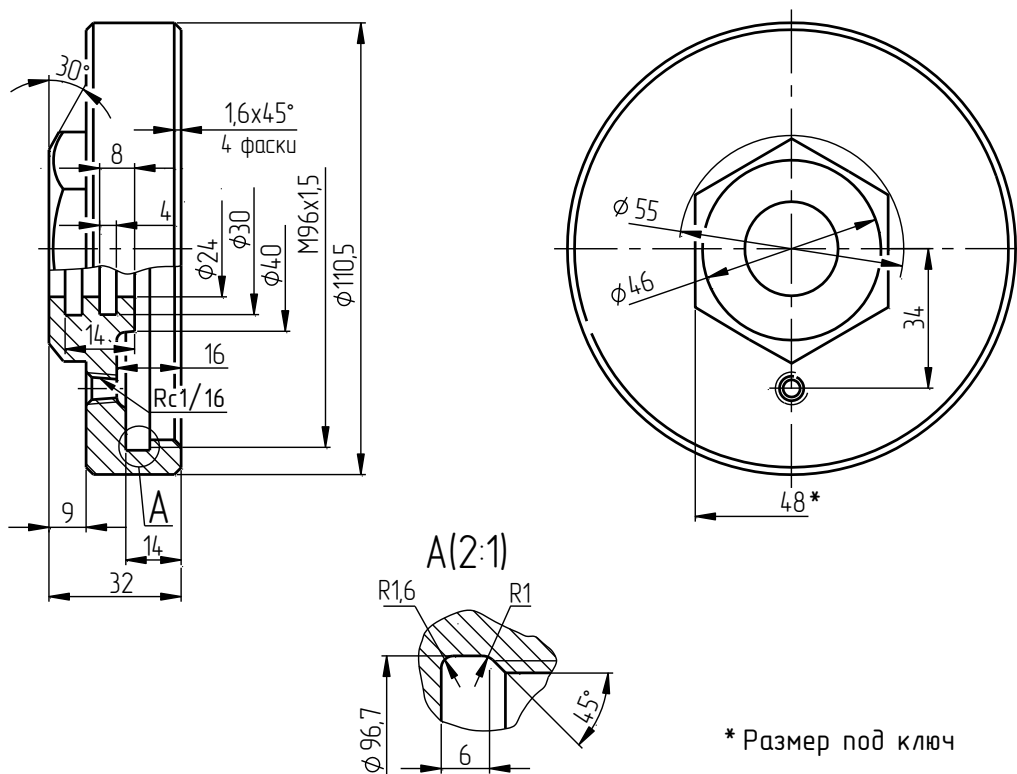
Прерывание линий чертежа в местах расположения размерных стрелок и чисел
